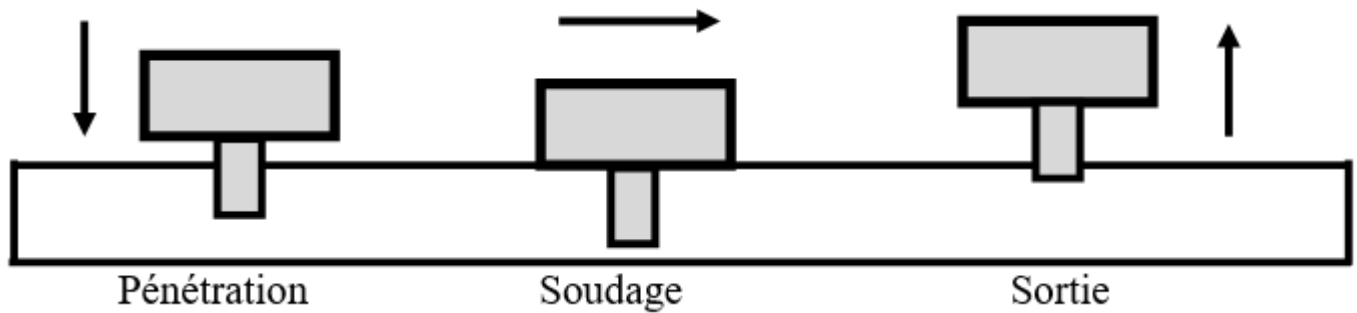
Principe général du procédé de soudage par friction malaxage
